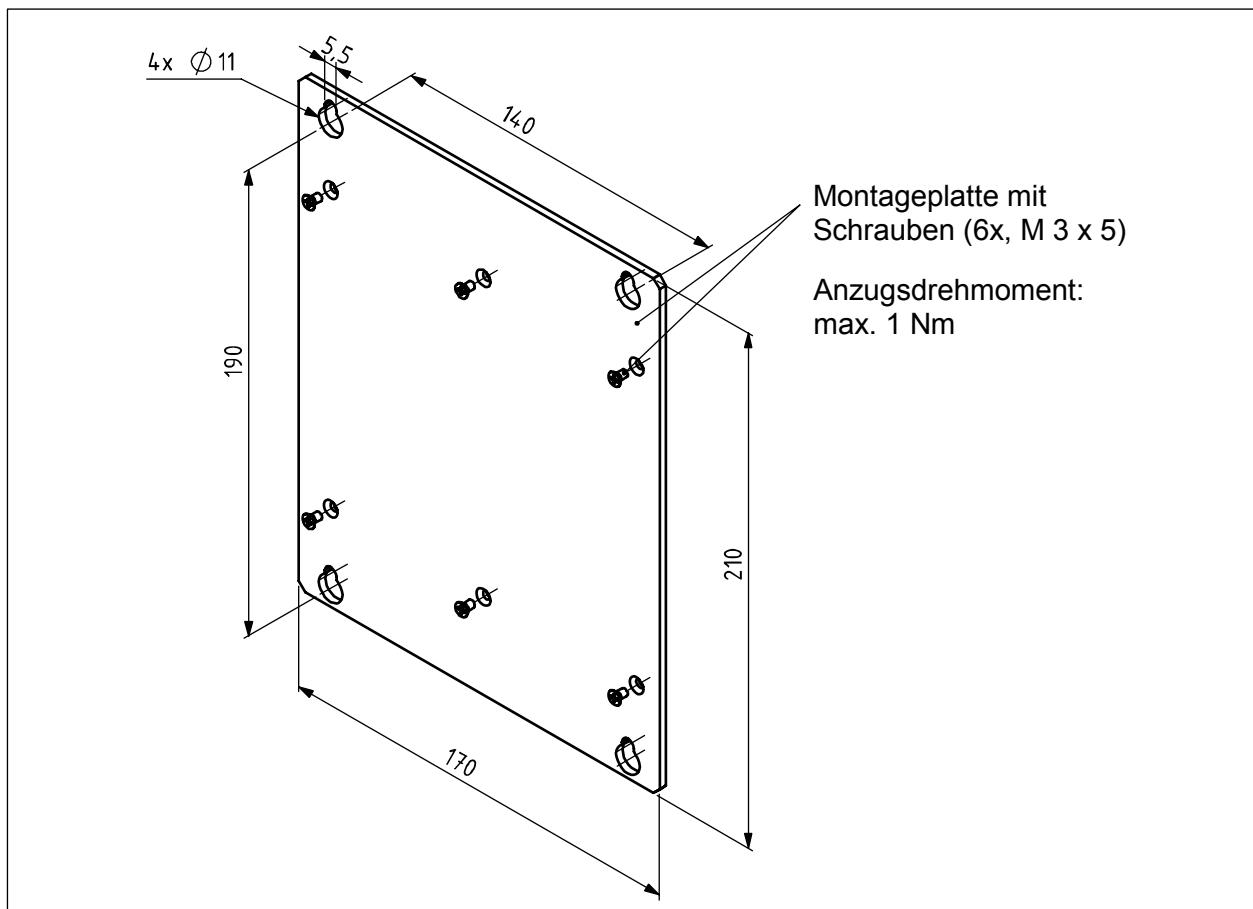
Montageplatte M-DS7000 RW – Abmessungen in Millimeter
